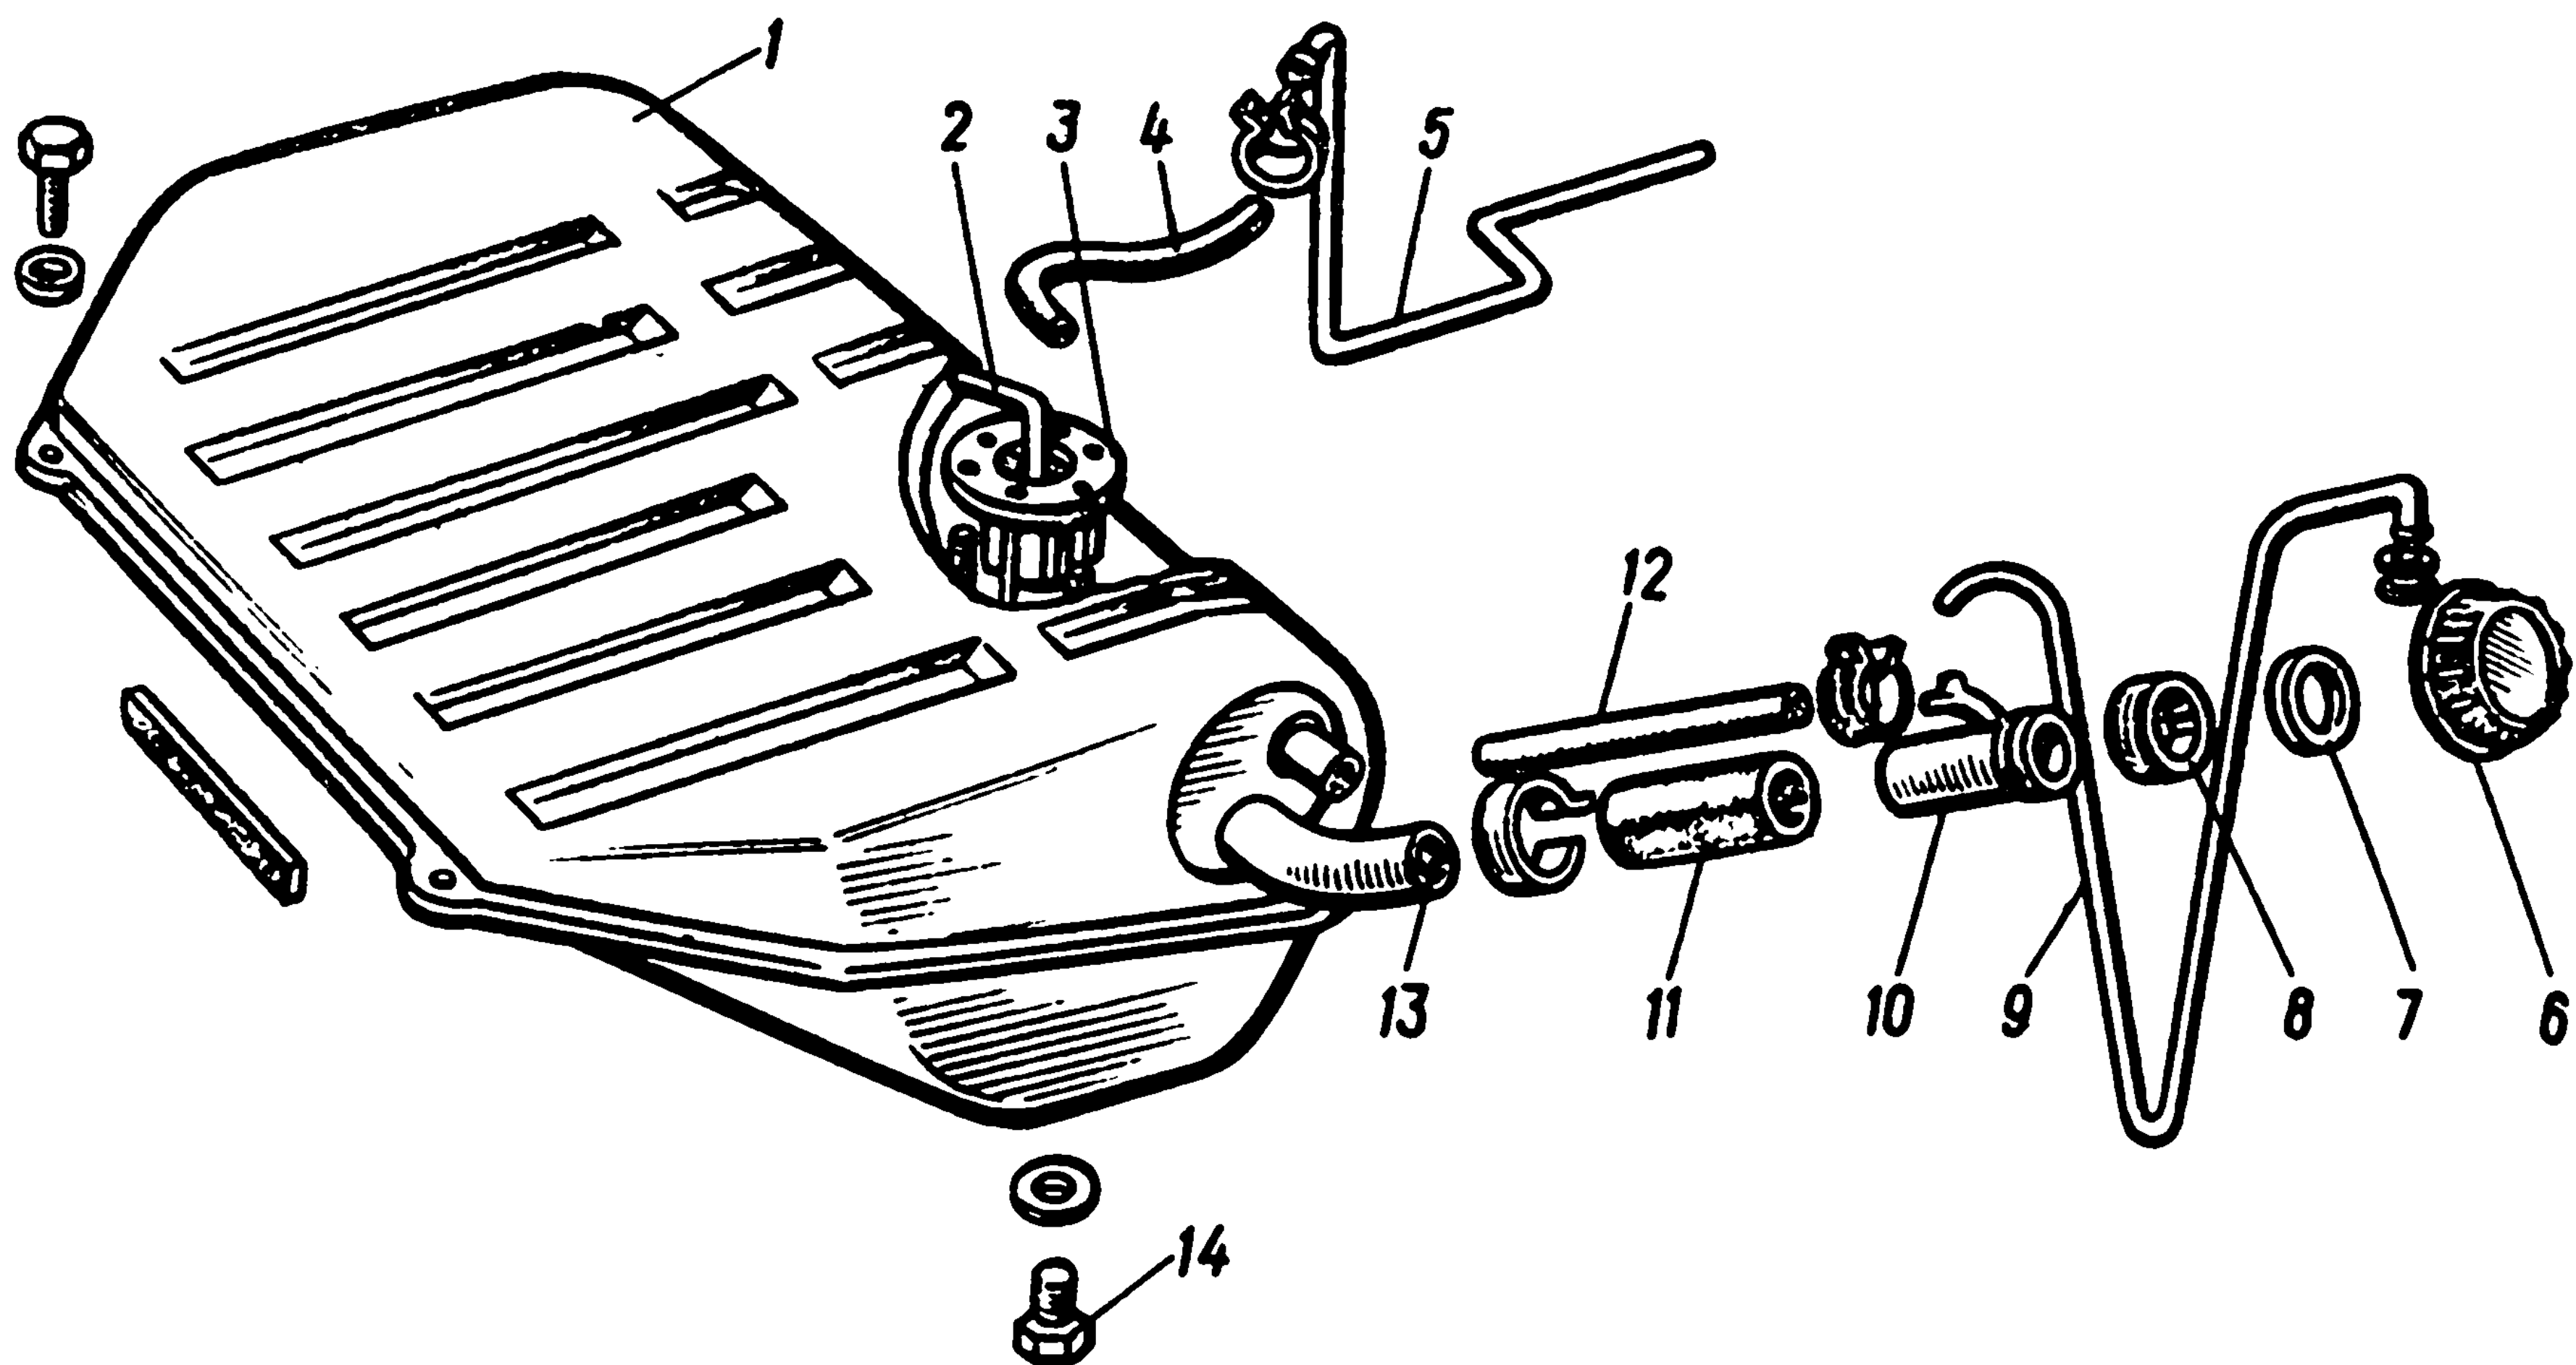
Топливный бак автомобиля ВАЗ-2121
